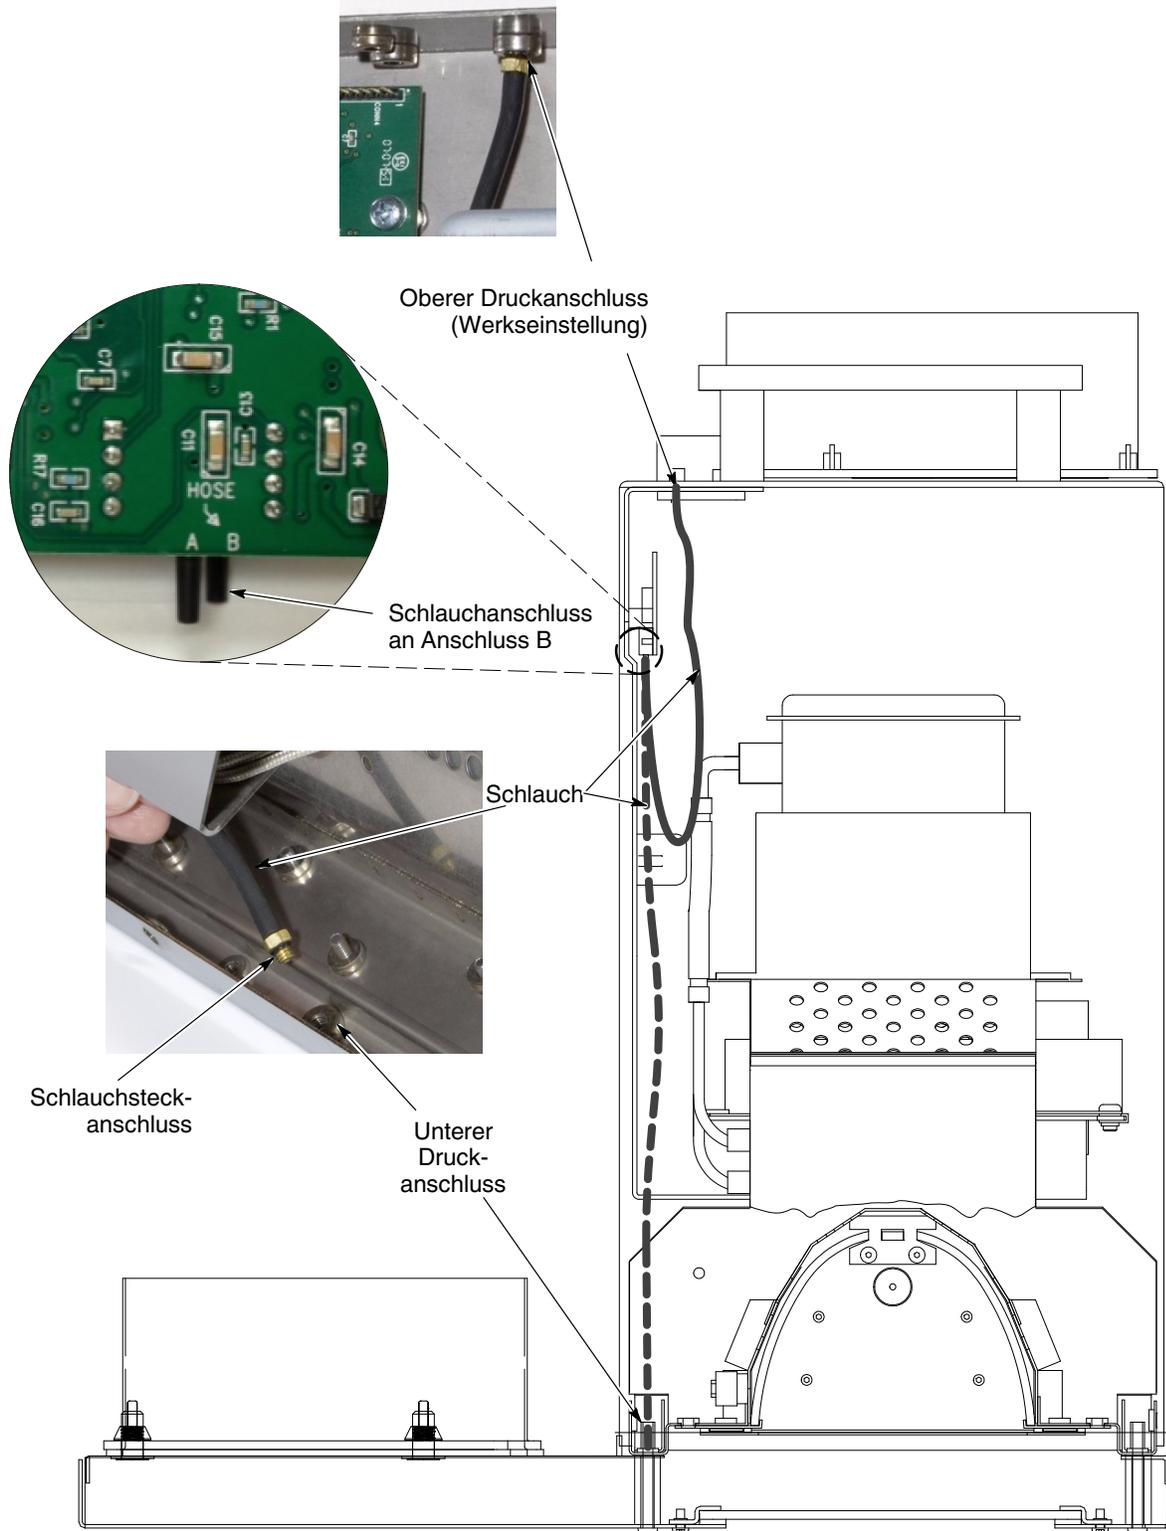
Druckanschlüsse – Ausführung mit externem Gebläse
